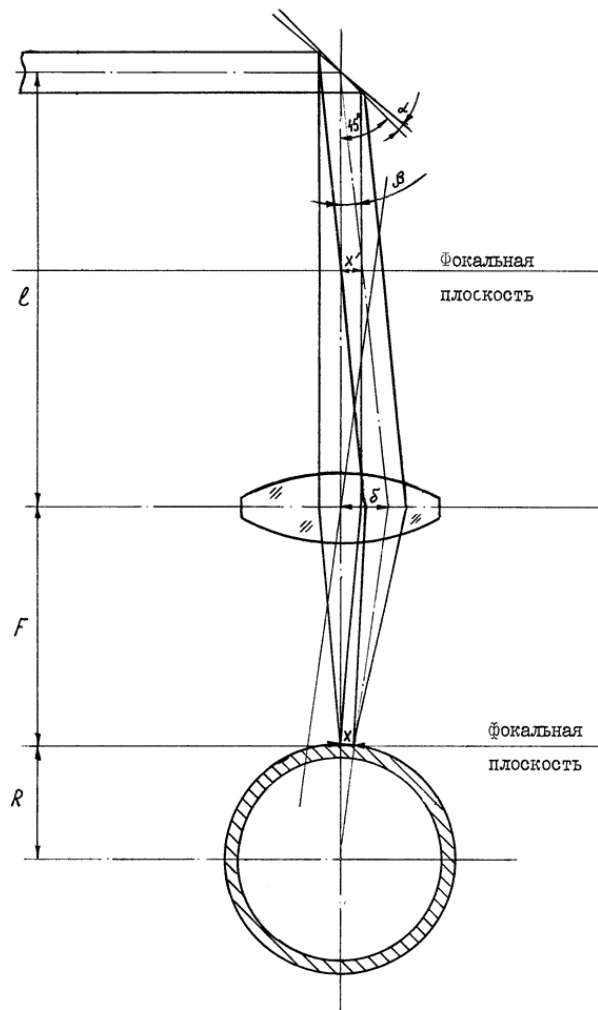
Предлагаемый способ лазерной сварки труб
